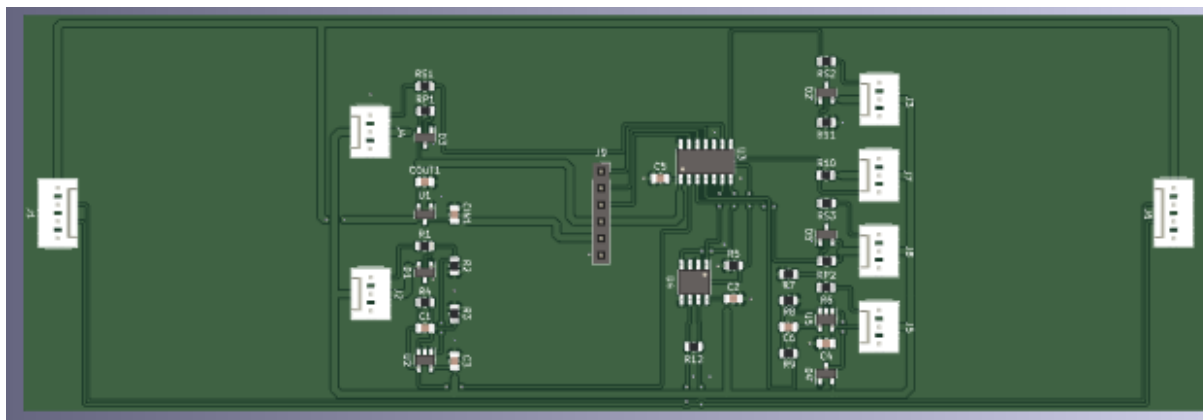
Diseño de PCB en KiCad. Fuente: Elaboración propia.
